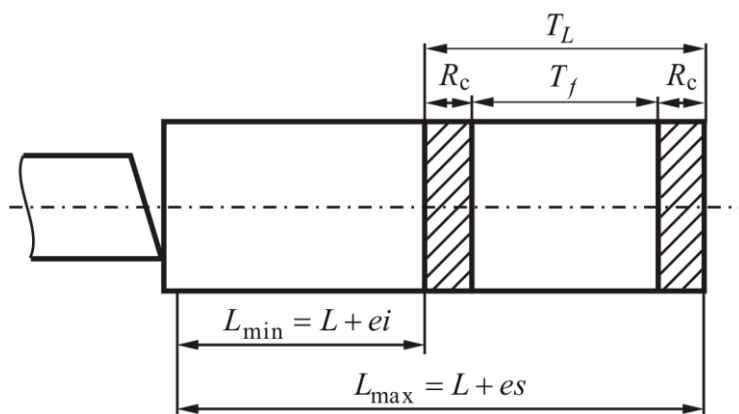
Предельные размеры детали и геометрическая погрешность станка R_c при $[u] = 0$ и $R = 0$; T_f – производственный допуск
